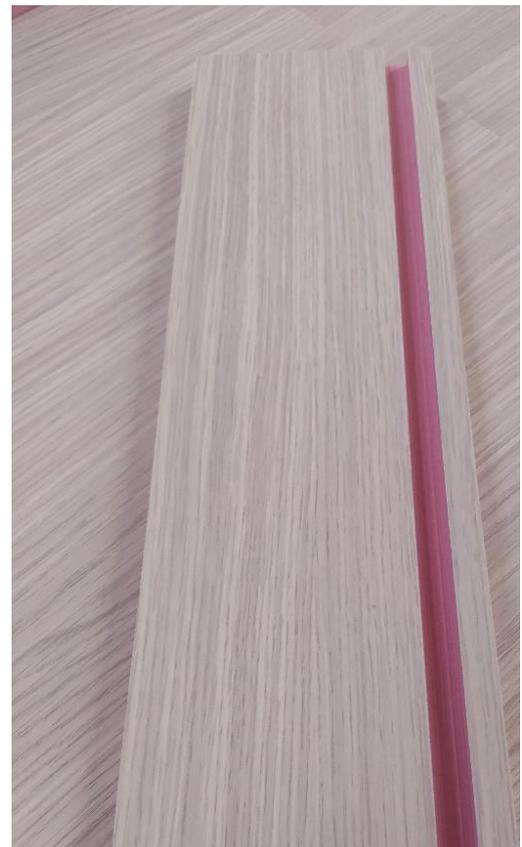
Rasgo de uma peça realizado pela máquina fresadora CNC (Foto de autores)
